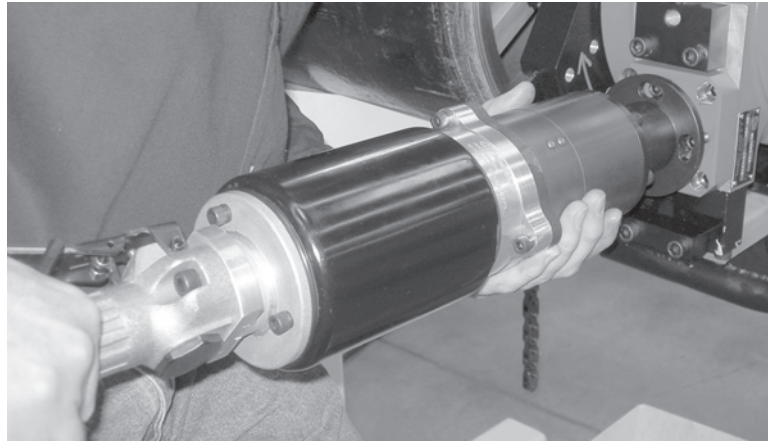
Installare la flangia motore sulle viti dell'adattatore motore.
